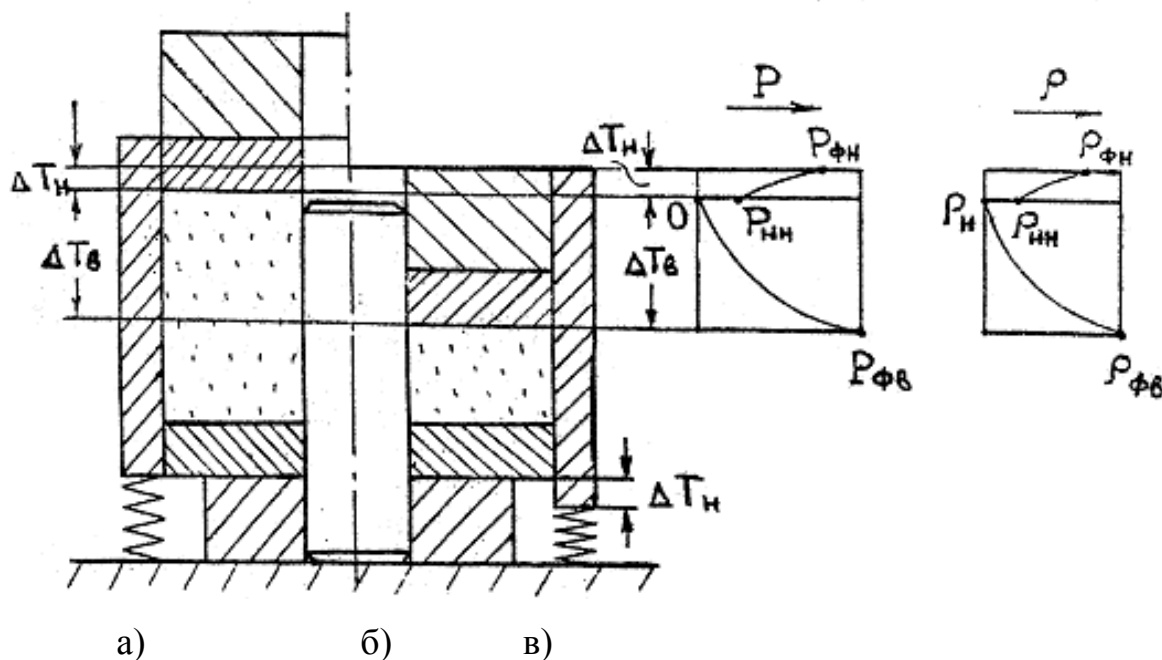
Схема одностороннего прессования с подпружиненной матрицей и подпрессовкой:
